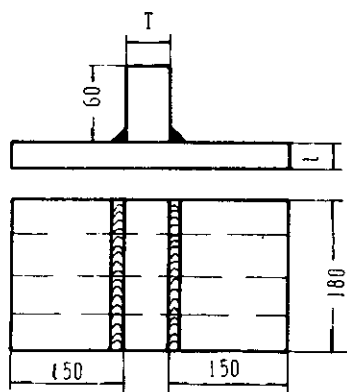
T 形接头角焊接接头试板的形状和尺寸
